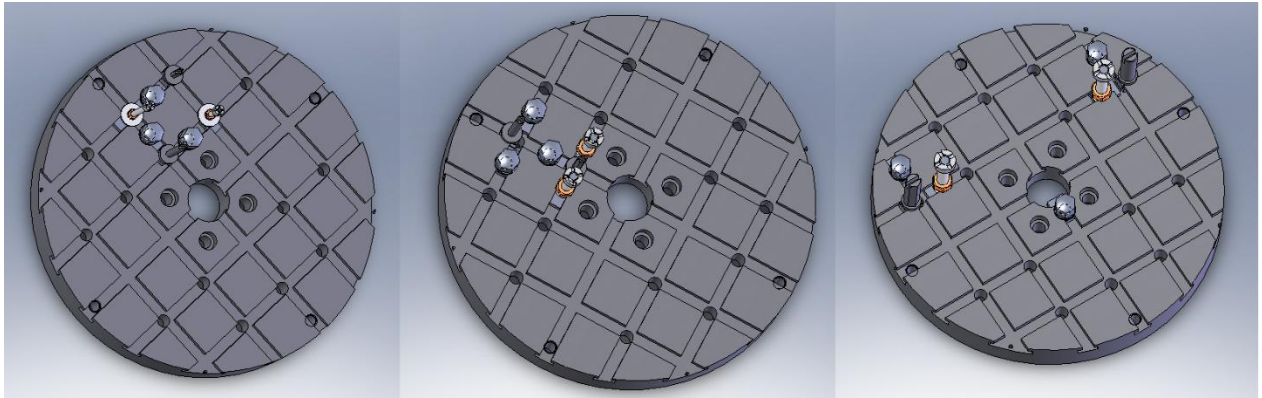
Зовнішній вигляд пристосування для обробки деталей «Кронштейн».
